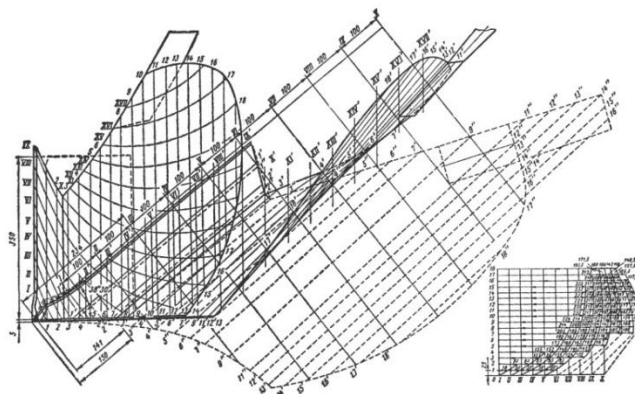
Полугвинтовий тип корпусу відвального плуга
